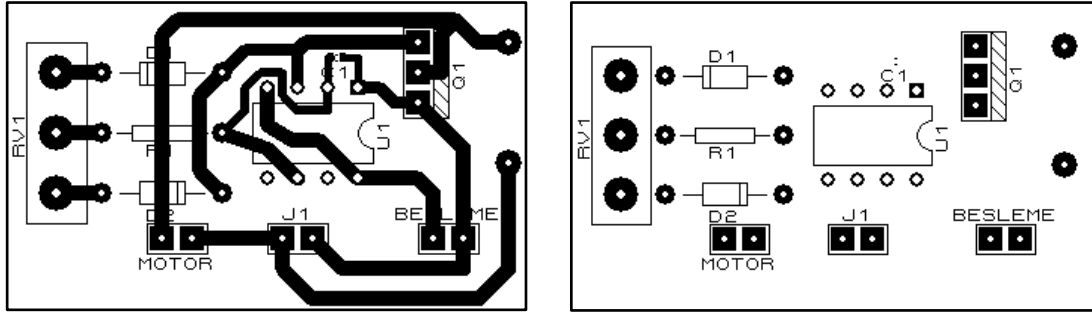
Doğru akım motoru hız kontrol devre şeması
